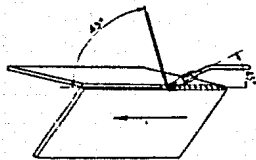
Soldadura en ángulo exterior.
